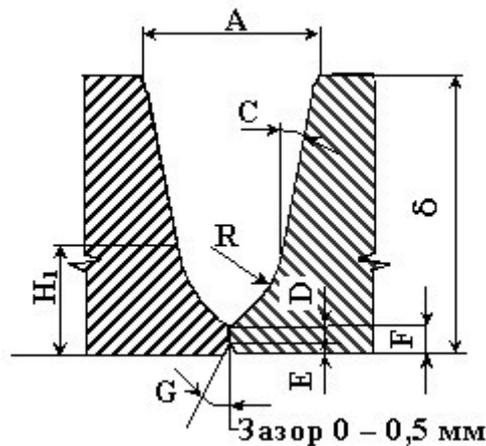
Схема сварного шва, выполненного автоматической сваркой с использованием двухдуговых головок"
